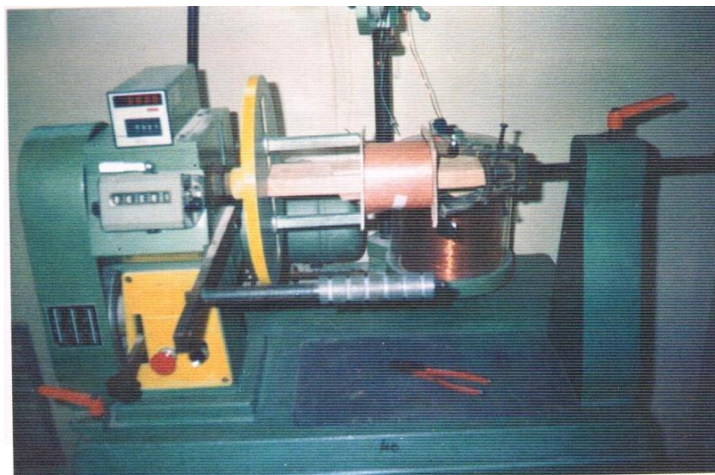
La fixation de la carcasse sur la machine [14]
